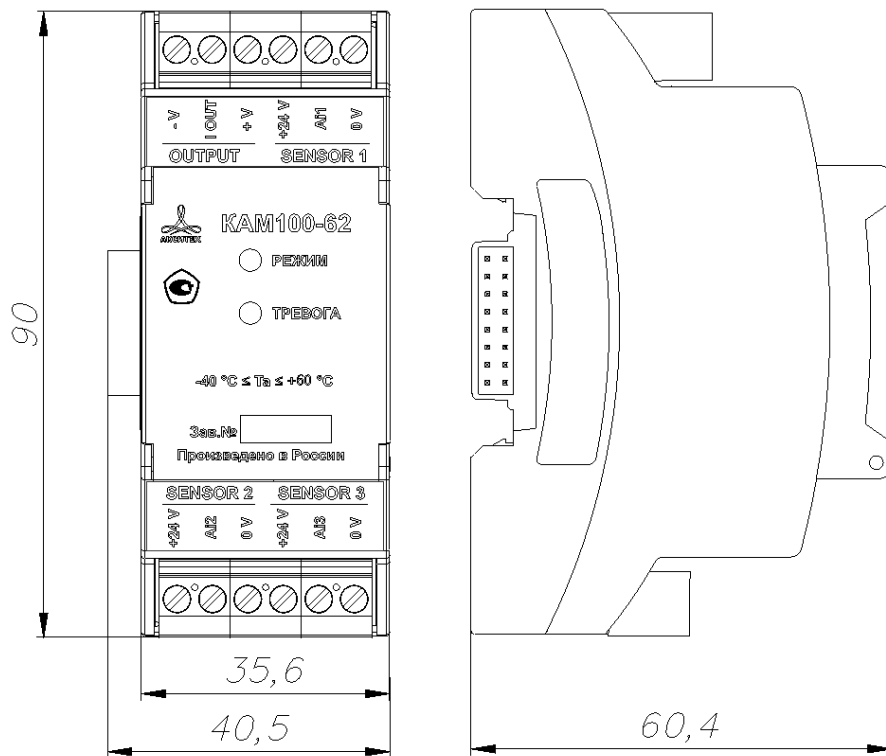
Внешний вид и габаритные размеры модуля 4-20 мА KAM100-62
